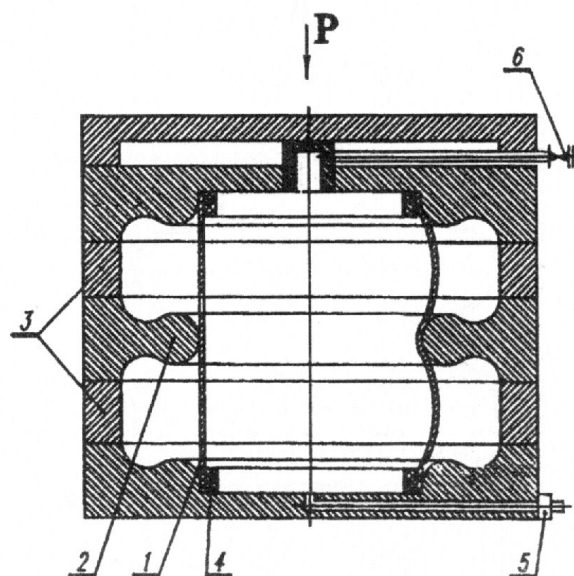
Штамп для гидроформовки сильфона: 1 — заготовка, 2 — кассета, 3 — ограничители (сухари), 4 — манжета, 5 — штуцера соединительных рукавов, 6 — вентиль
